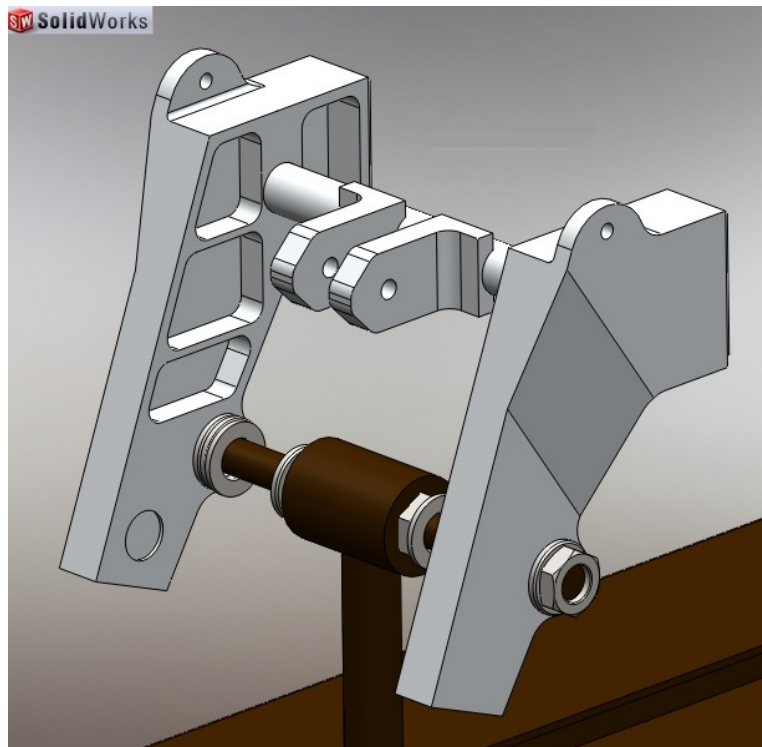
Soldadura del tubo con las pletinas
